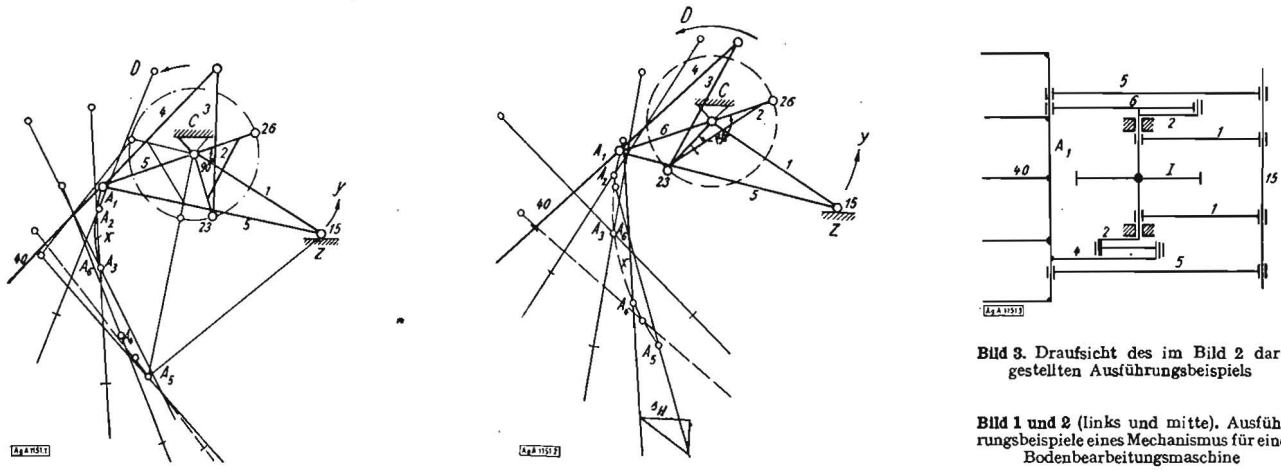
Draufsicht des im Bild 2 dargestellten Ausführungsbeispiels
